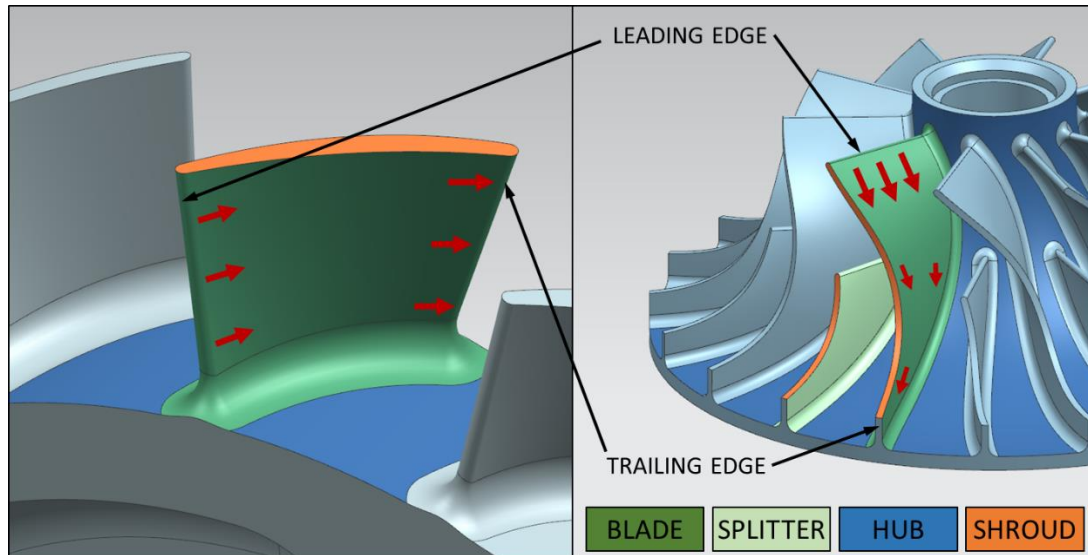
5 Nomenclatura de geometrías de blisk e impeller (Diseñadas en el módulo CAD de NX)
